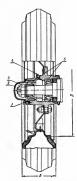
Регулировка подшипников и правляющего колеса трактора «Беларусь»:
